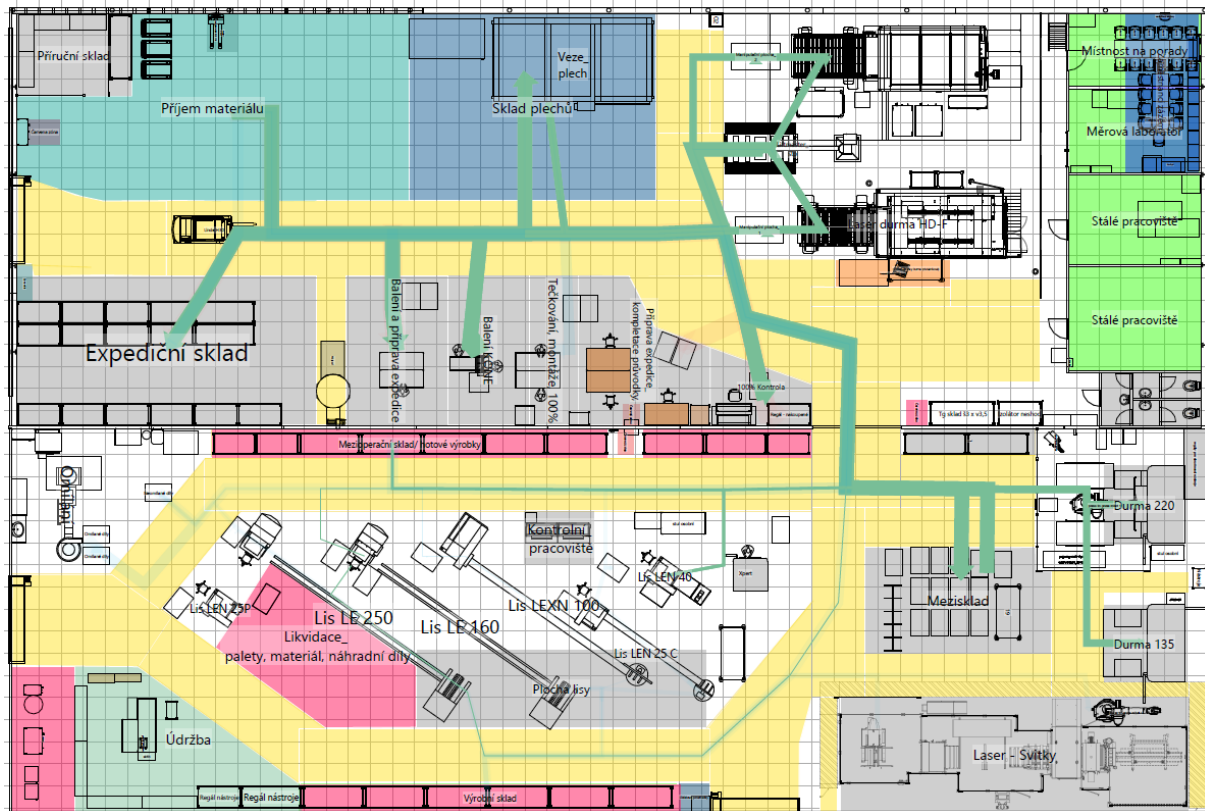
Layout haly včetně využitých ploch - Varianta 3
